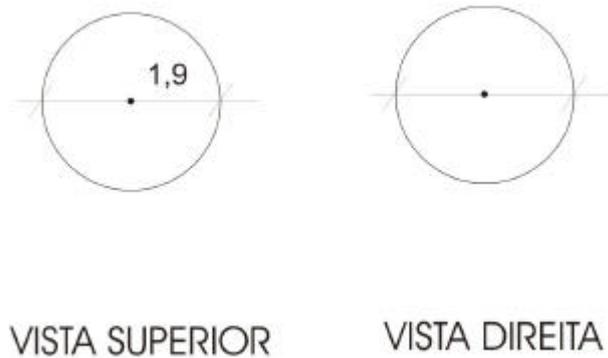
Desenho técnico do ovo de mesa, dimensões em cm
